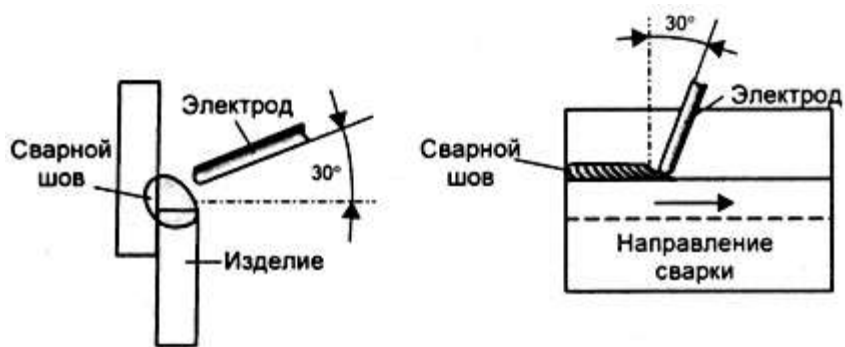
Сварка нахлесточного соединения в горизонтальном положении.
